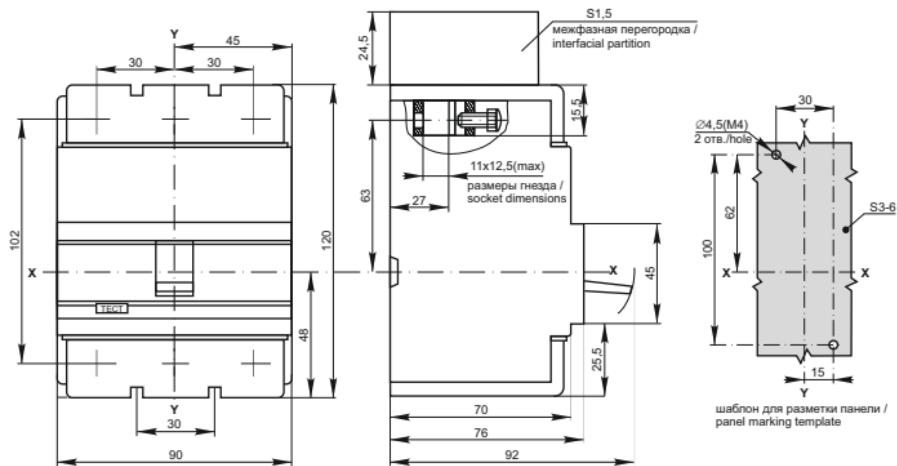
Габаритные и установочные размеры выключателя BA88-33 /
